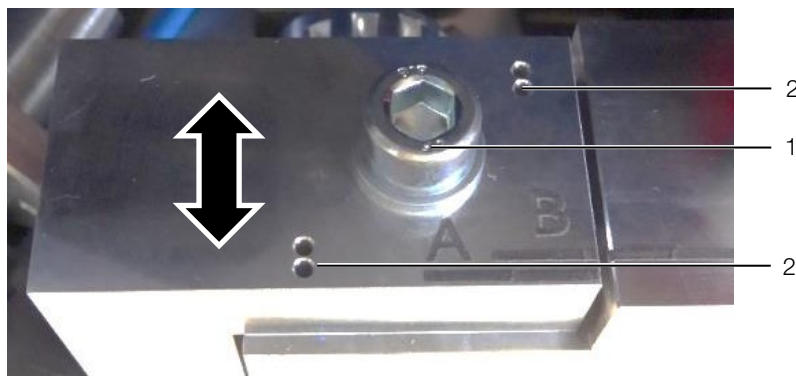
réglage de la cale d'ouverture (réglé : B)
